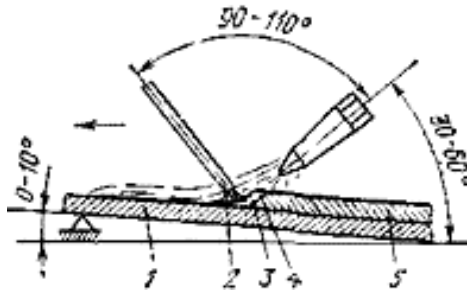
Схема газопламенной наплавки: 1 – основной металл; 2 – присадочный пруток; 3 – жидкая ванна; 4 – пленка флюса; 5 – наплавленное покрытие
